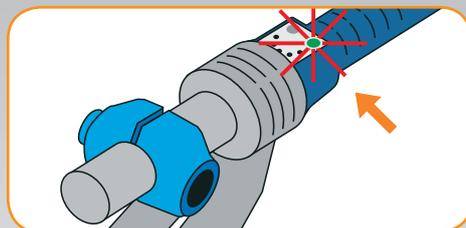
Сварочный аппарат для полифузной сварки. При правильной рабочей температуре светится индикатор.
